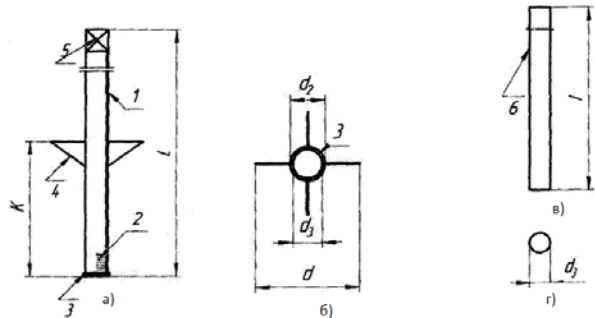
Схема реалізації розробленого способу розкриття льотки доменних печей: 1 – порожній корпус довжиною L; 2 – кернорвач; 3 – вінець твердосплавних різців; 4 – розширювач діаметром d; 5 – бурильні труби; 6 – металевий стрижень довжиною l та діаметром  $(d_2+d_3)$ .
